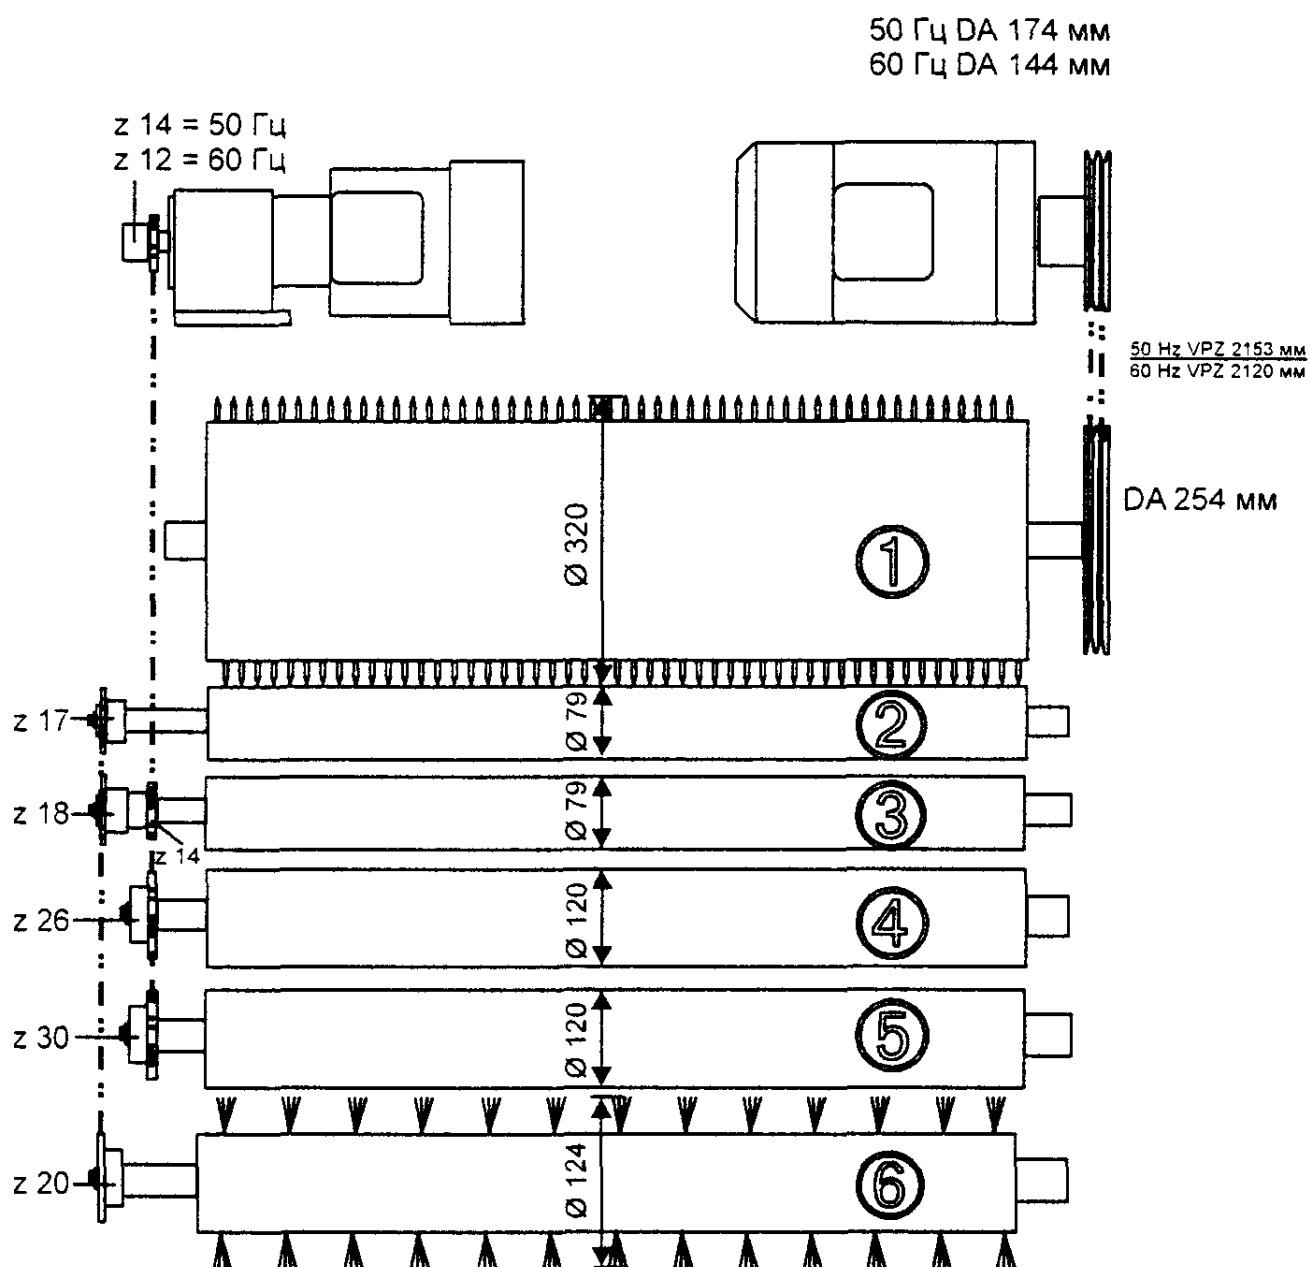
Кинематическая схема разрыхлительного устройства смесителя UNibend:
